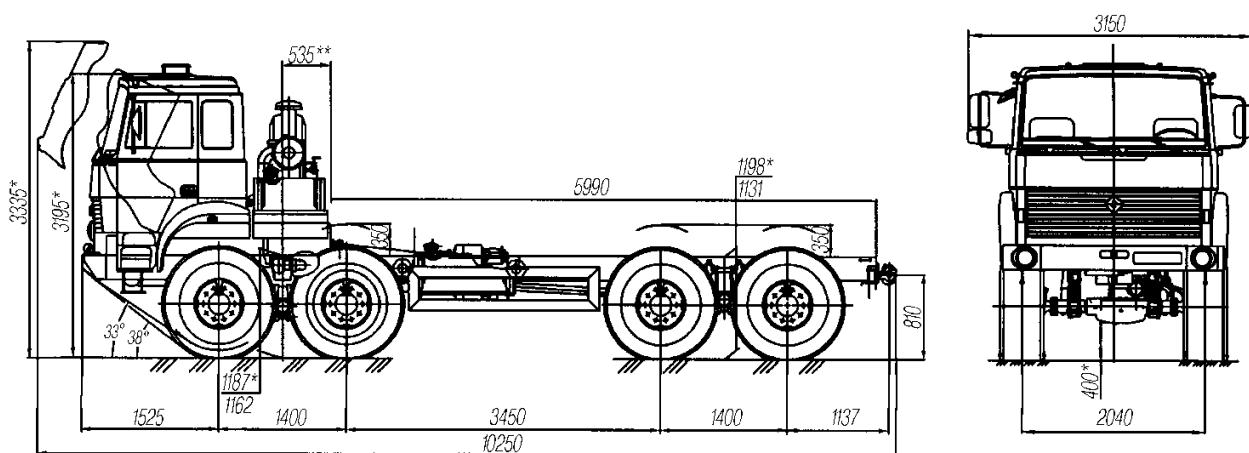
Габаритные размеры шасси Урал-532361-70
